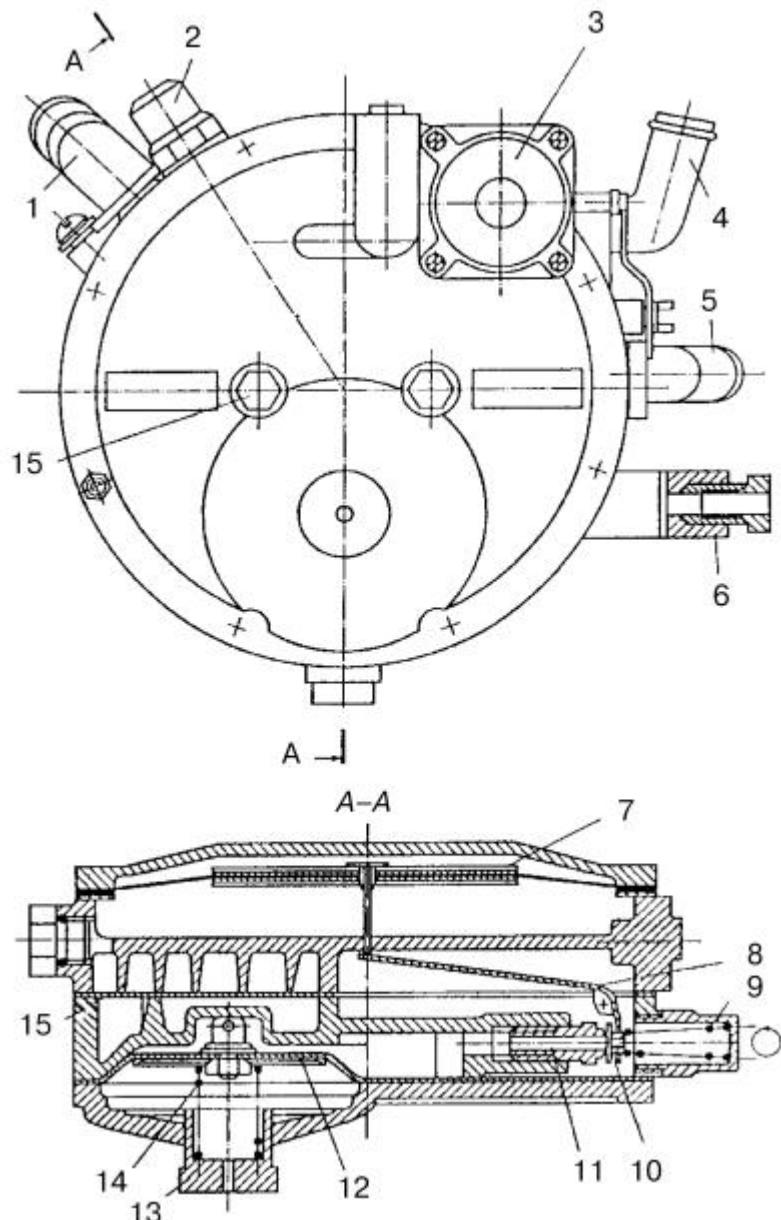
Схема редуктора-испарителя низкого давления ОАО «Компрессор»: 1 – патрубок выхода газа; 2 – крышка пружины; 3 – пневматический клапан холостого хода; 4, 5 – штуцеры подвода и отвода теплоносителя; 6 – входной газовый штуцер; 7 – диафрагма второй ступени; 8 – рычаг клапана второй ступени; 9, 14 – пружины; 10 – клапан второй ступени; 11 – седло клапана второй ступени; 12 – диафрагма первой ступени; 13 – стакан – камера теплоносителя; 15 – болты.
